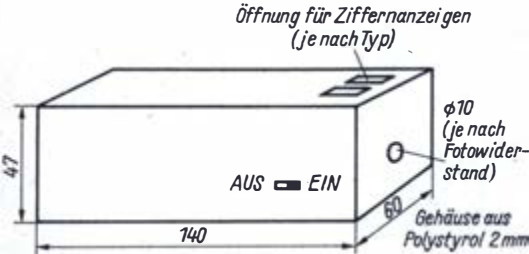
Gehäusekonstruktion des Drehzahlmessers
